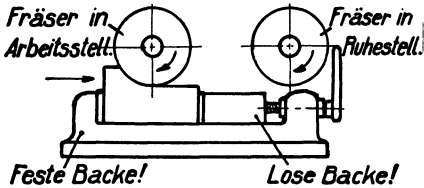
Schema der Frserstellung zum gewhnlichen Maschinenschraubstock auf der Frsmaschine.
